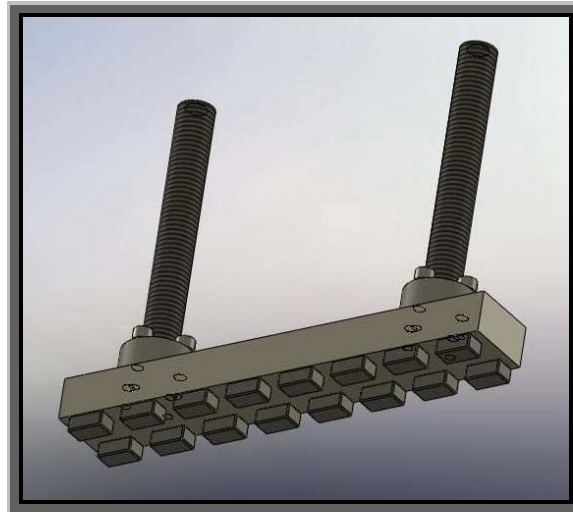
Vista isométrica del tornillo y tuerca del conjunto rueda giratoria.
